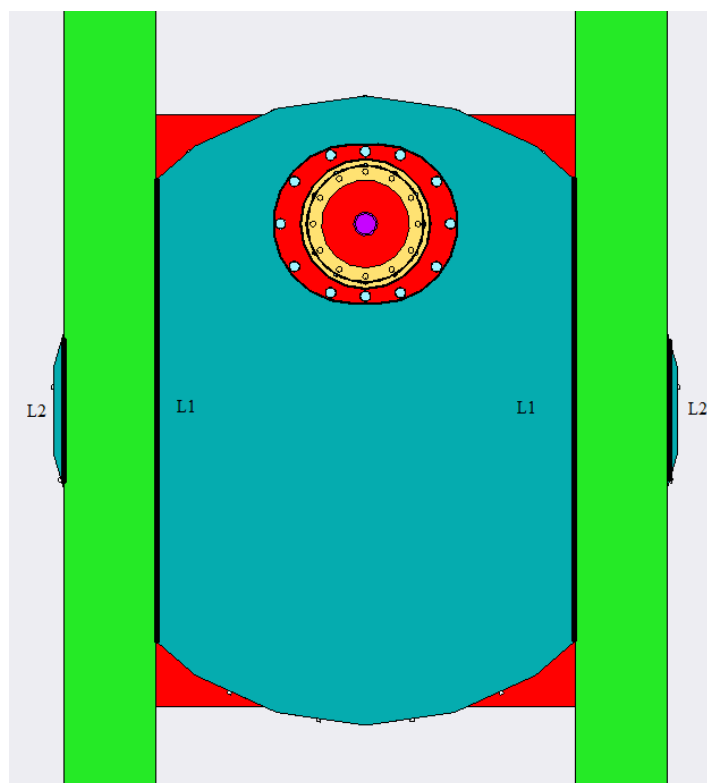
Cordones de soldadura unión pluma-placa superior.
